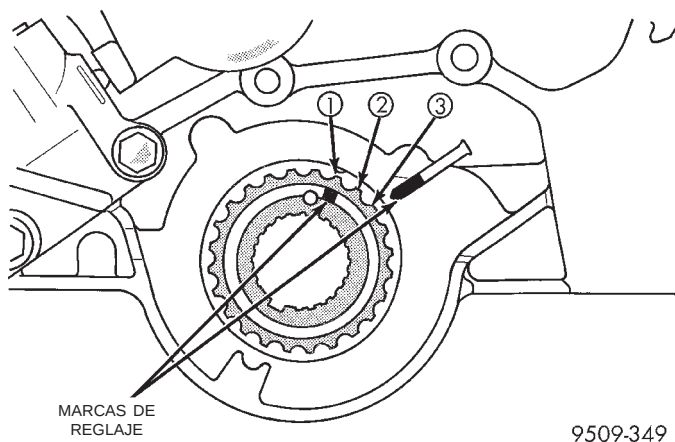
Sincronización de la rueda dentada del cigüeñal
